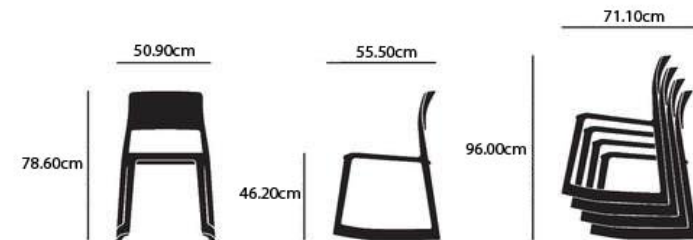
Planimetría del Mobiliario. “Sillas Tip Top ®”, Vitra, 2012
